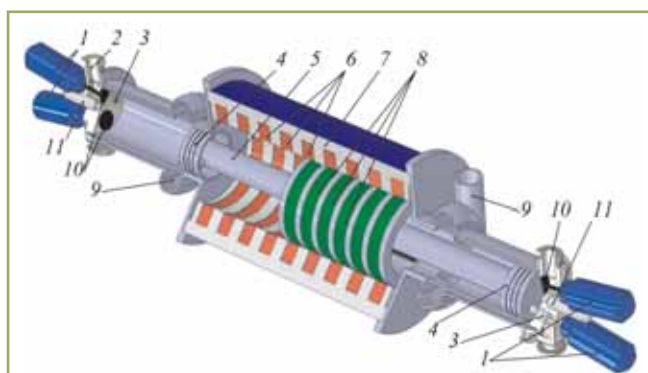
Линейный генератор со свободным поршнем (ЛГСР): 1 – электропривод клапана; 2 – выпускное отверстие; 3 – свеча зажигания; 4 – поршень; 5 – шток; 6 – катушки статора; 7 – магнитопровод статора; 8 – постоянные магниты; 9 – впускной патрубков; 10 – клапан; 11 – инжектор
